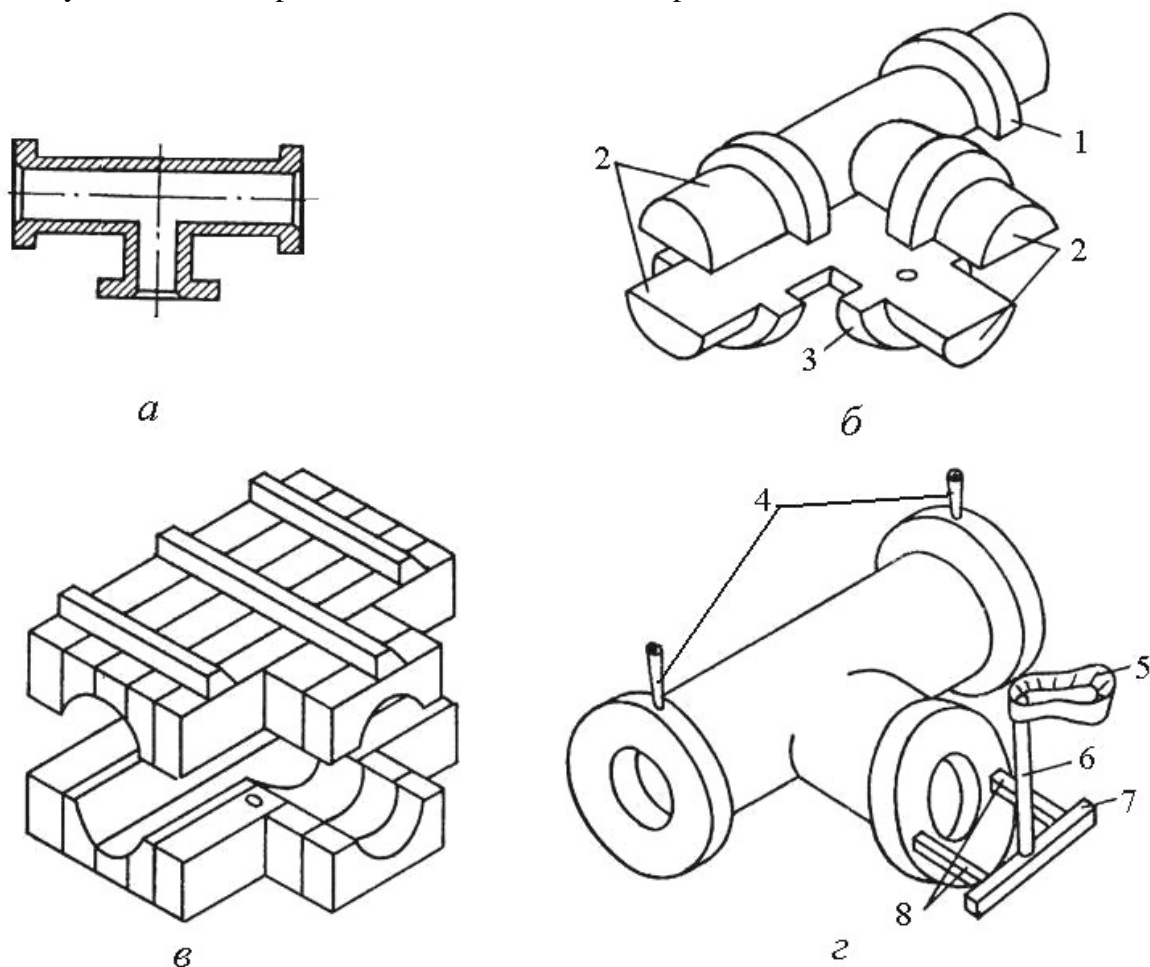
Формовка в двух опоках: а – чертеж отливки; б – модель; в – стержневой ящик; г – отливка с литниковой системой: 1, 3 – верхняя и нижняя половины модели; 2 – стержневые знаки; 4 – выпоры; 5 – литниковая чаша; 6 – стояк; 7 – шлакоуловитель; 8 – питатели
